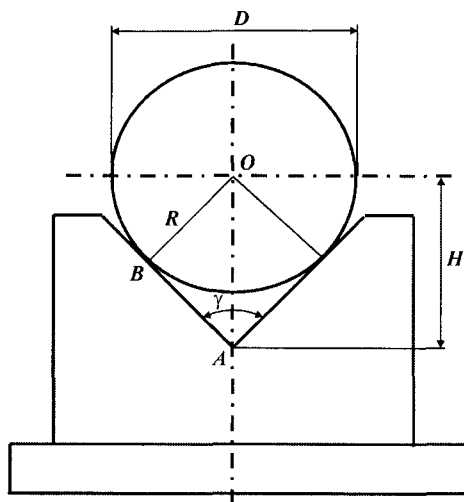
Схема базирования заготовки с главной базой, имеющей вид цилиндрической наружной поверхности, на призму.
